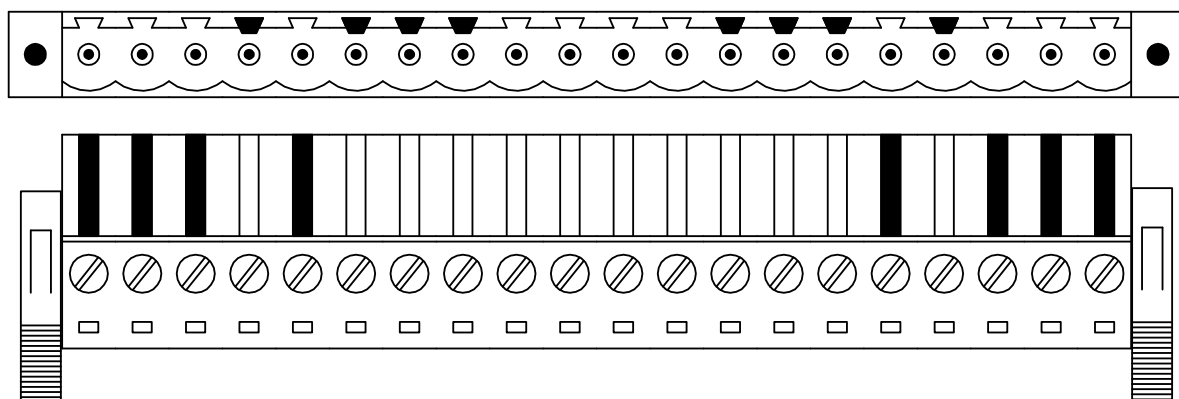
Zasunutí kódovacího elementu do tělesa konektoru
